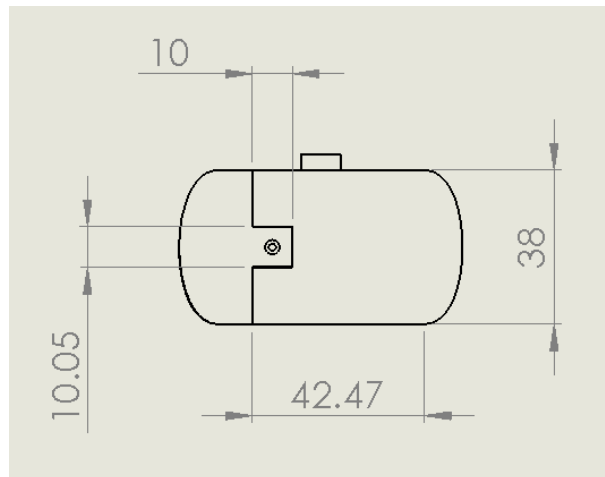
Plano de la vista inferior del dispositivo. Todas las cotas están en mm.
